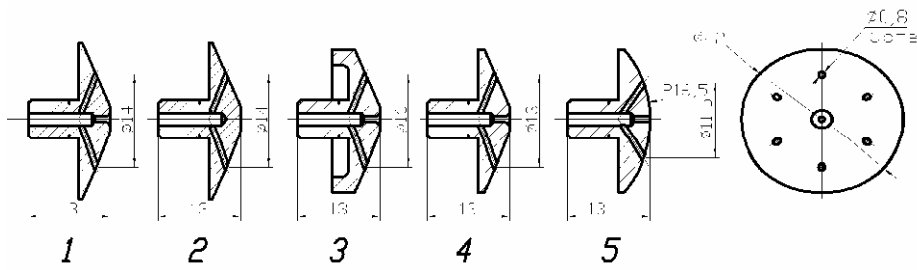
Рабочие инструменты с круглой формой излучающей поверхности
